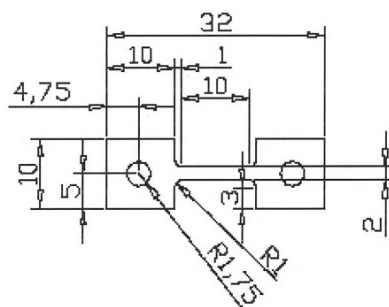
Géométrie et dimensions (en mm) de l'éprouvette étudiée (épaisseur 1mm).
